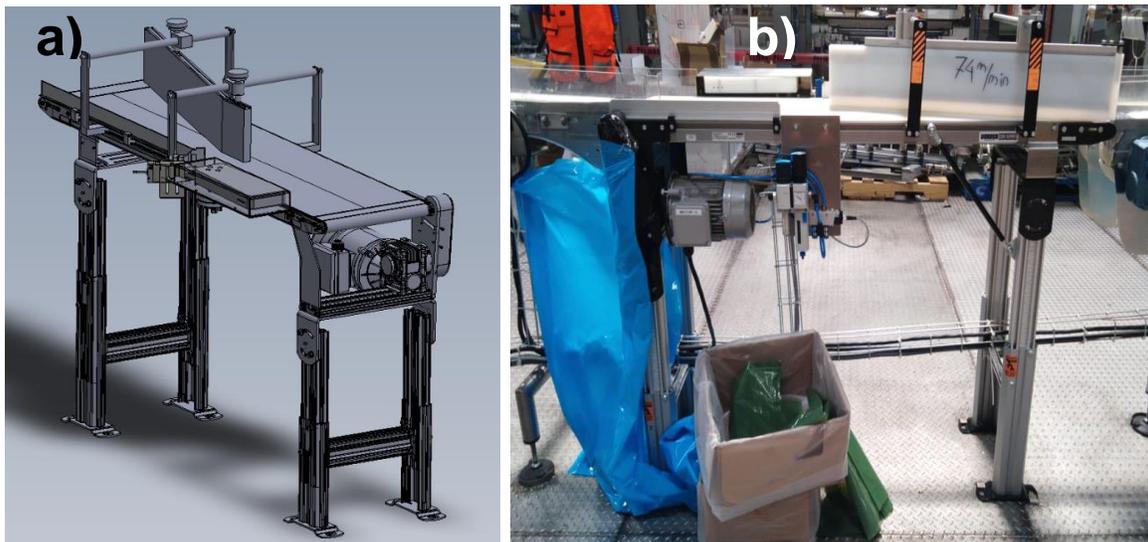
Ensamble 3D de guías ajustables, a) Diseño 3D en SolidWorks, b) Equipo en operación
